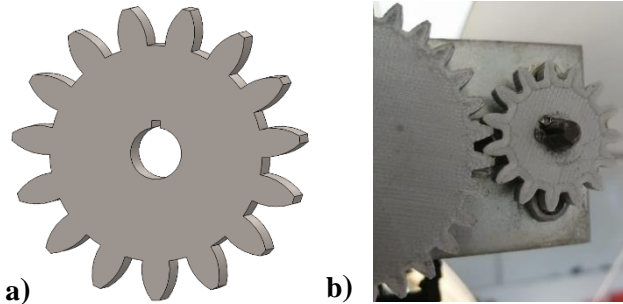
a) Desenho 3D engrenagem 15 dentes b) Impressão da engrenagem 15 dentes
